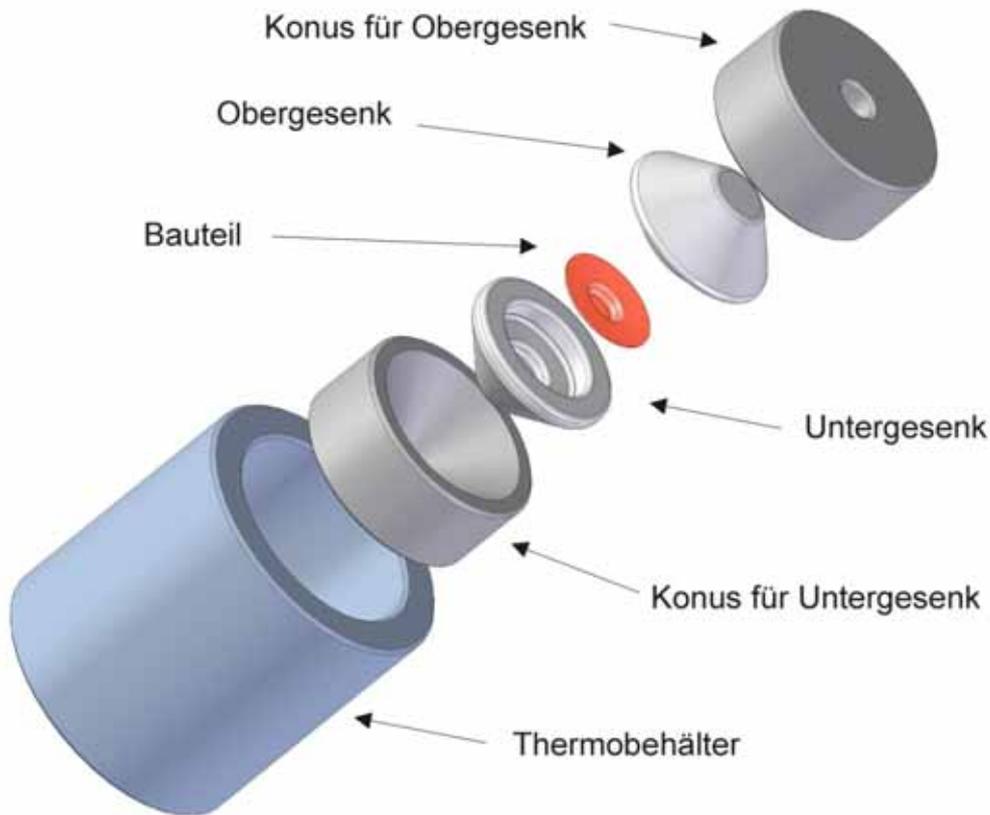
Explosionsmodell des Schmiedewerkzeug für das Isothermschmieden
